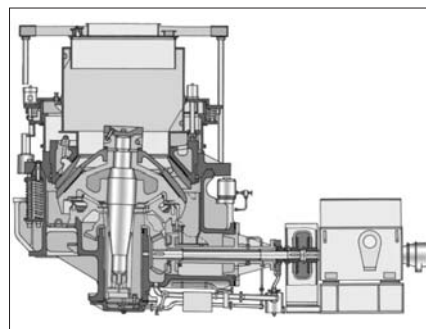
Общий вид дробилки КМД-2200Т7-Д
